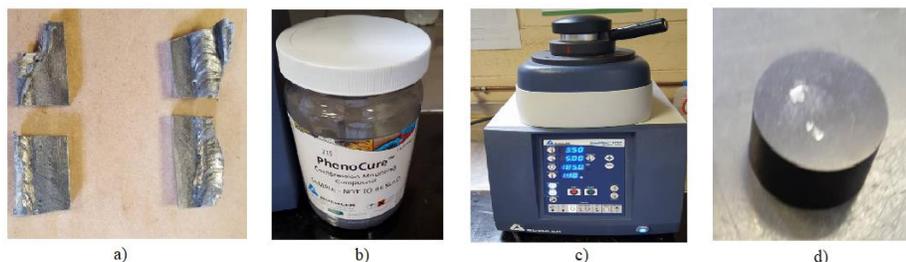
Realización de portamuestras: a) Corte en extremo periféricos del área soldada, b) Baquelita utilizada para portamuestra, c) Máquina de portamuestra BUEHLER en proceso y d) Proceso de portamuestra terminado
